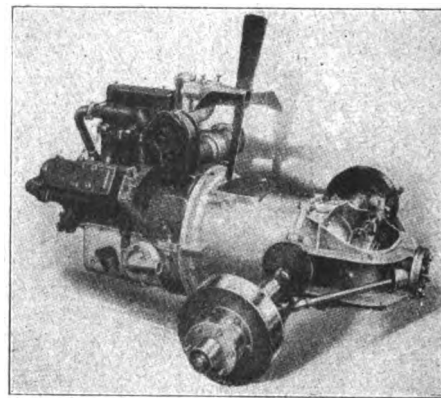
»Motortriebachse« mit schwingender Hinterachse.
